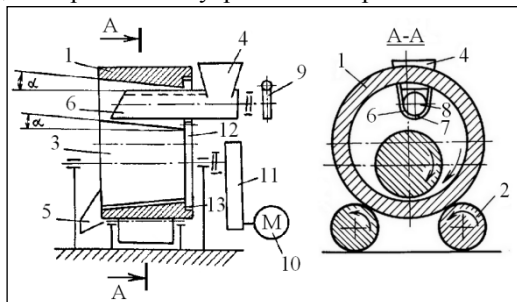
Конструкция измельчителя: 1 – кольцо; 2 – роликовая опора; 3 – валок; 4 – загрузочный узел; 5 – разгрузочный узел; 6 – желоб; 7 – выпускная щель; 8 – шнек; 9 – привод; 10 – мотор; 11 – редуктор
